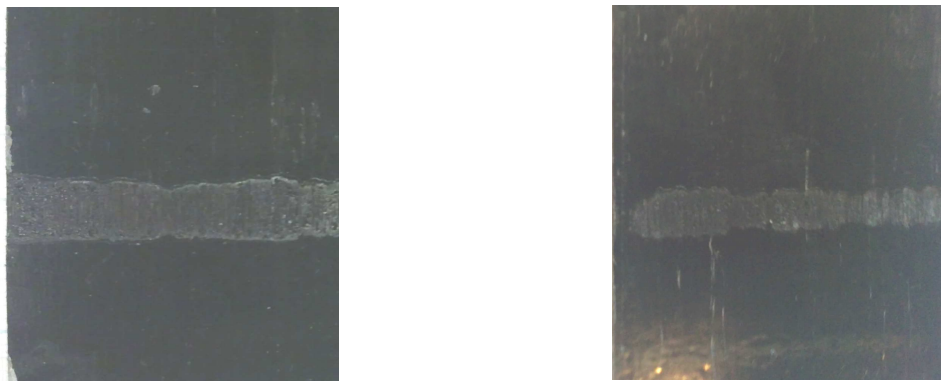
Surfaces soudées de deux éprouvettes E90.
